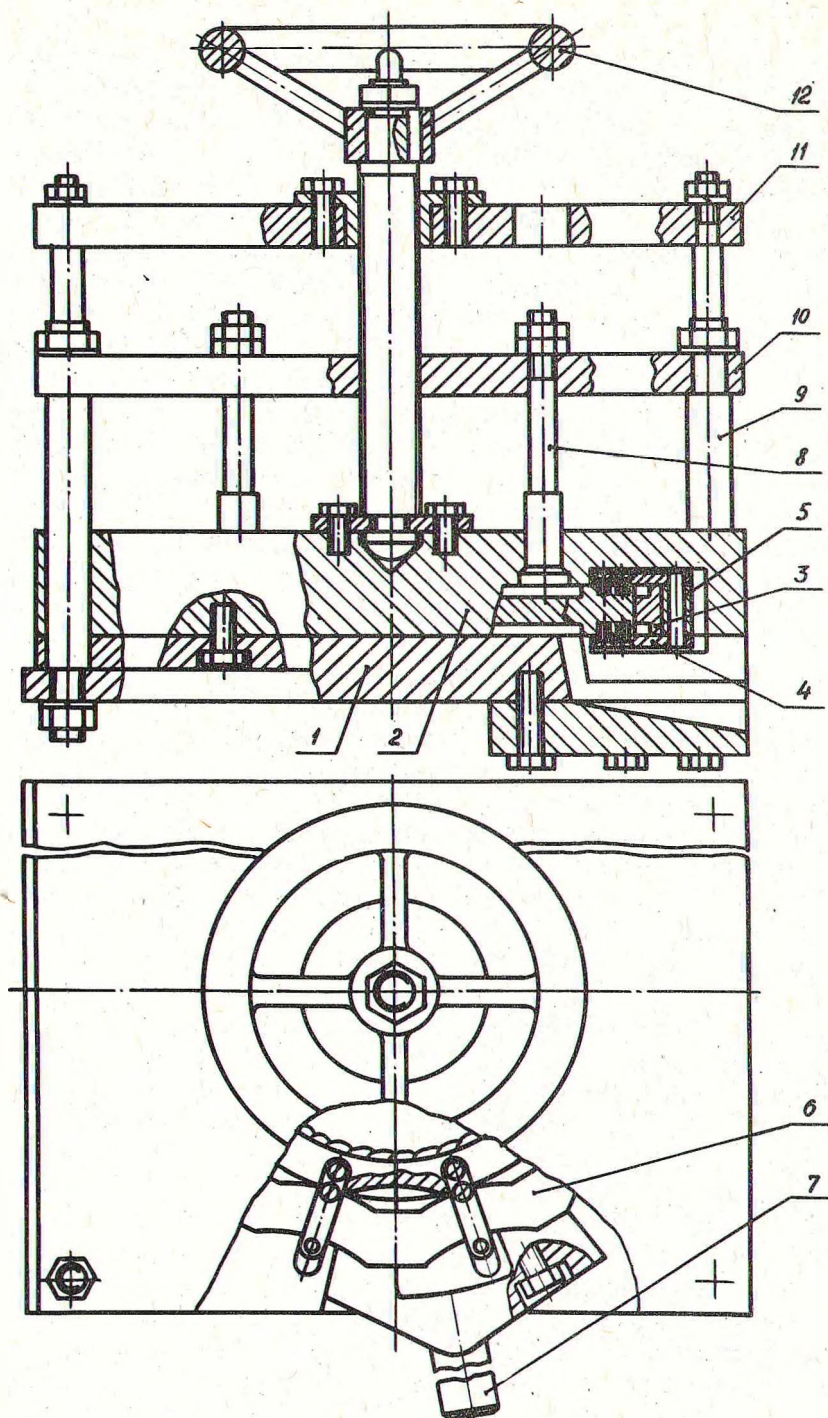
Кокиль для отливки колец с рифленным ручьем.
